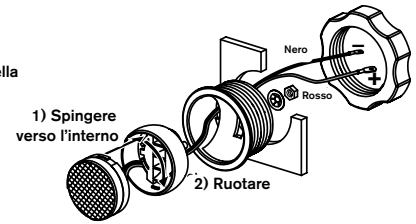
Montaggio del woofer a portiera e del tweeter su plancia. (TWEETER sulla plancia WOOFER nella predisposizione)
